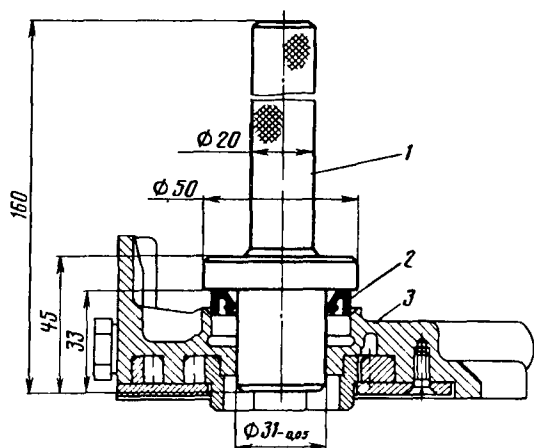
Запрессовка манжеты в корпус масляного насоса:
